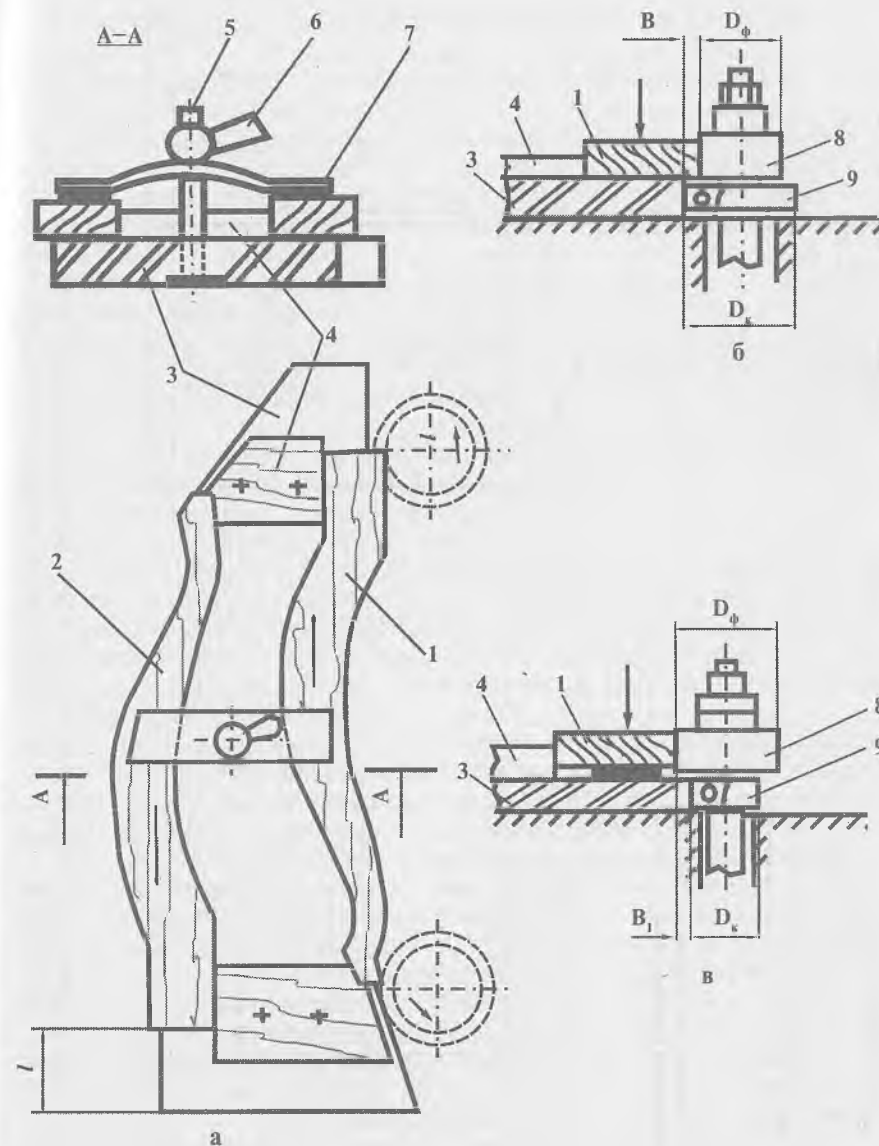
Фрезерование заготовок криволинейных деталей на фрезерных станках в шаблоне:
